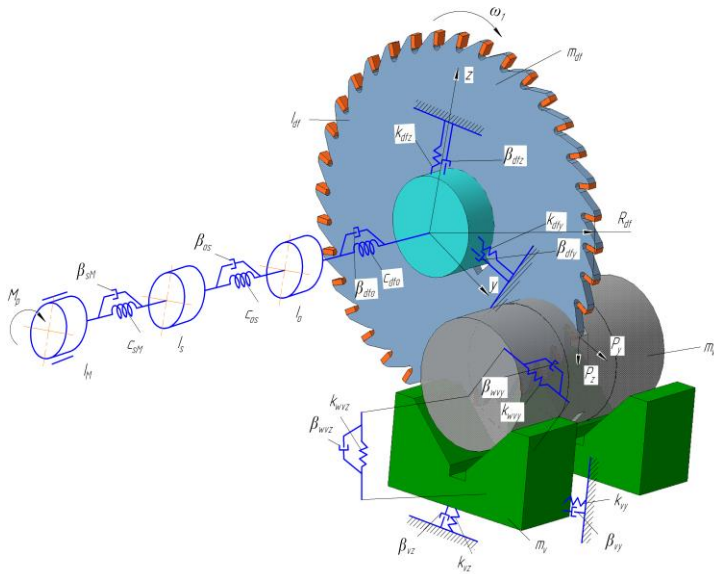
Схема динамічної моделі різання циліндричної заготовки дисковою фрезою на фрезерно-відрізному верстаті
